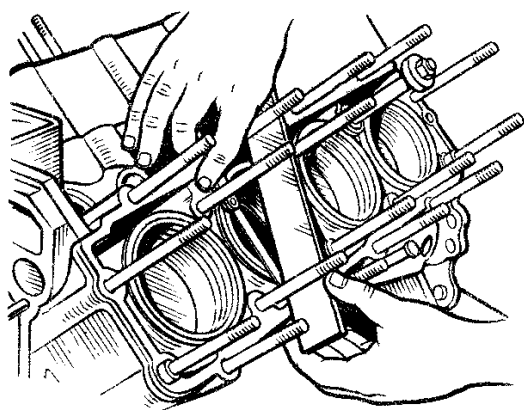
Проверка величины утопания гильзы в блоке цилиндров
